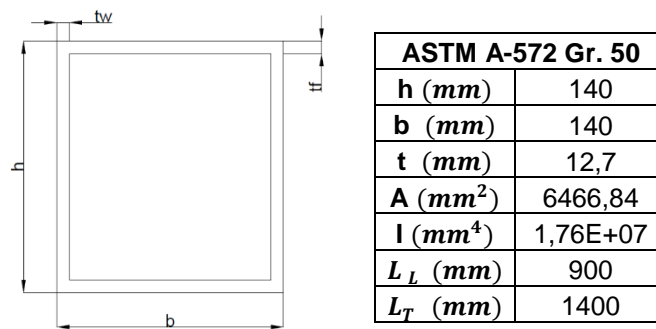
Propiedades Vigas Cajón para Estructura del Carro.
